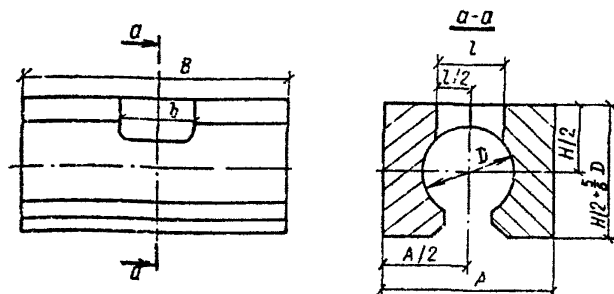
Конструкция медных полуформ для сварки соединений верхнего ряда спаренных стержней, собранных "вразбежку".
